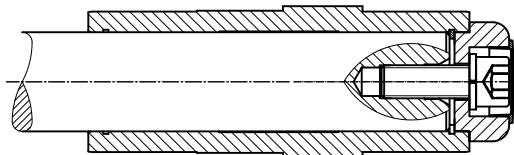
Закрепление редуктора на валу без буртика с помощью фиксирующего элемента
